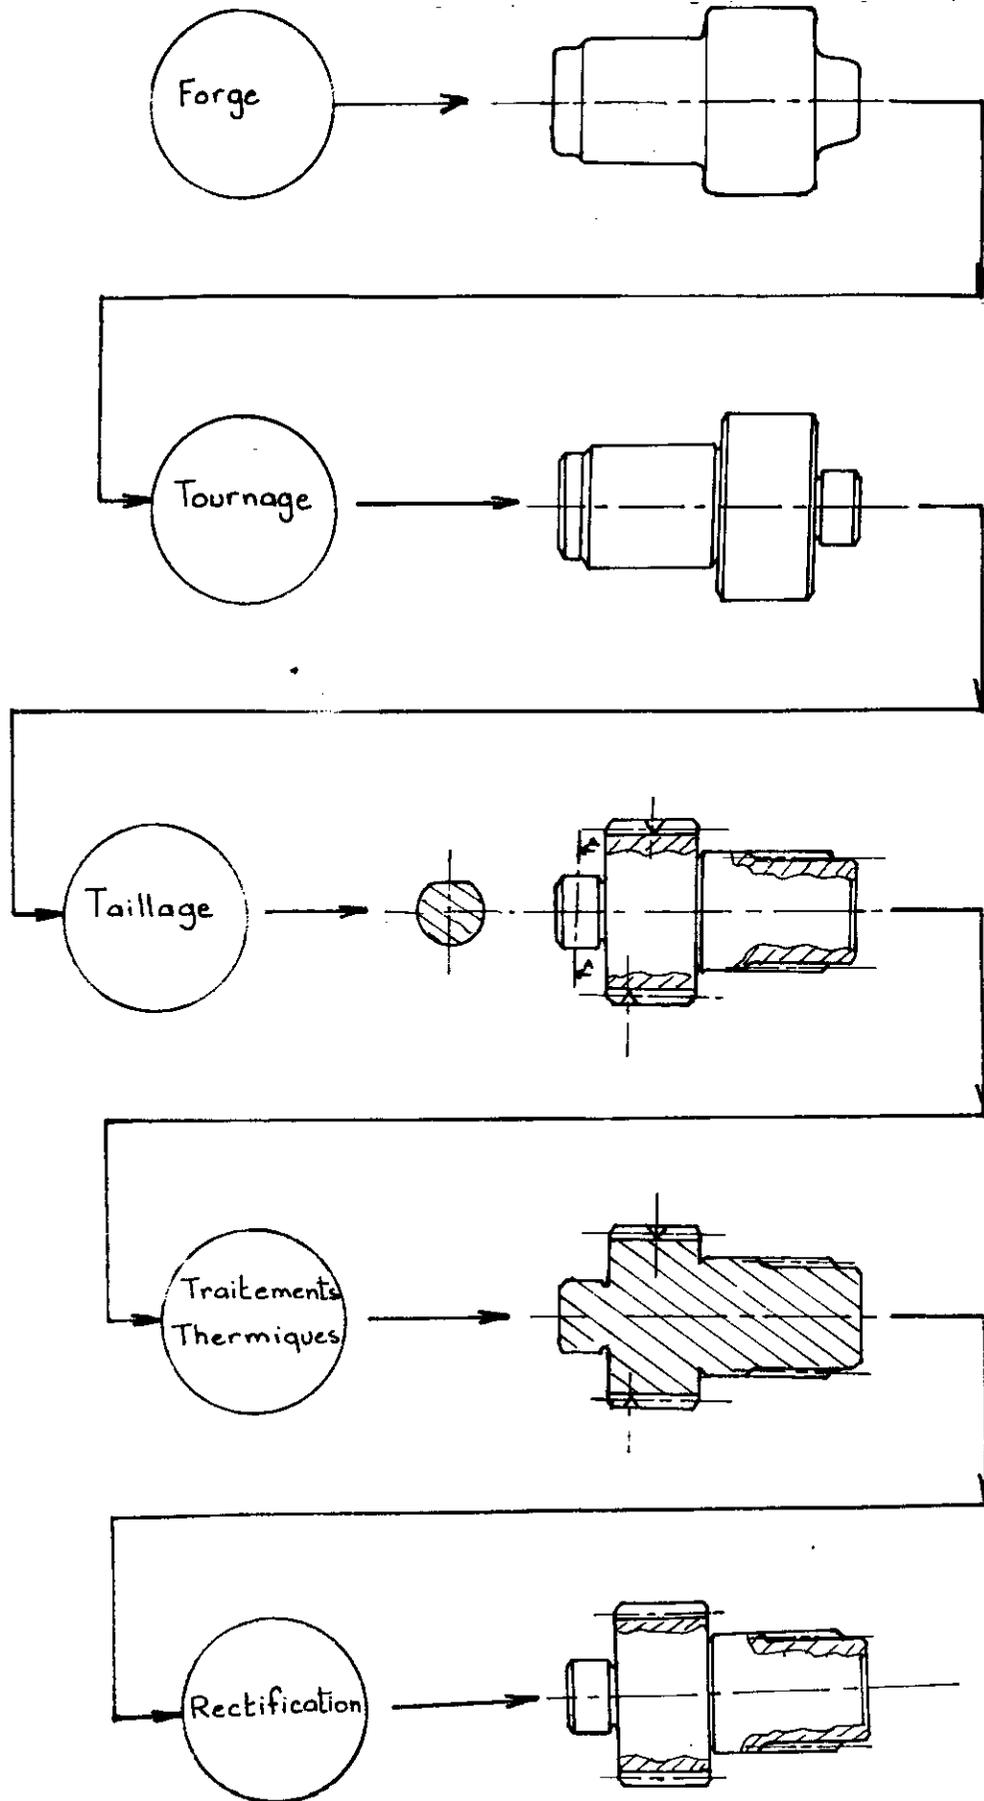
Procédé de fabrication de l'arbre de crabotage (166053).
